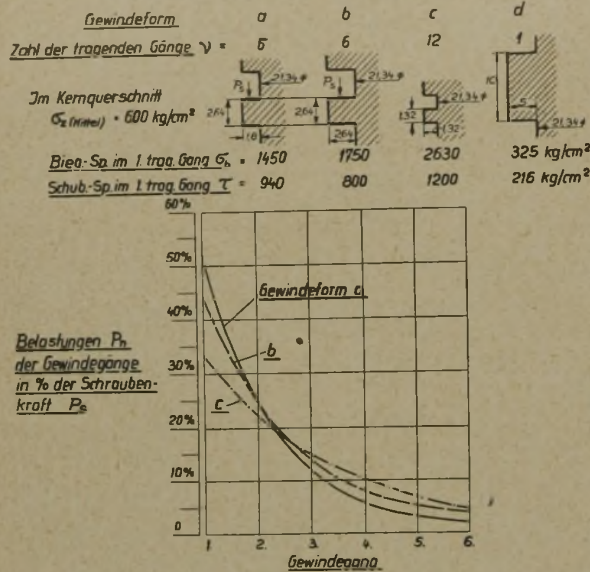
Gewindebelastungen bei verschiedenen flachgängigen Gewindeformen.
